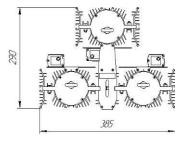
Габаритный чертеж светильника Econex Hell (360 70°C/ 180 100°C)
